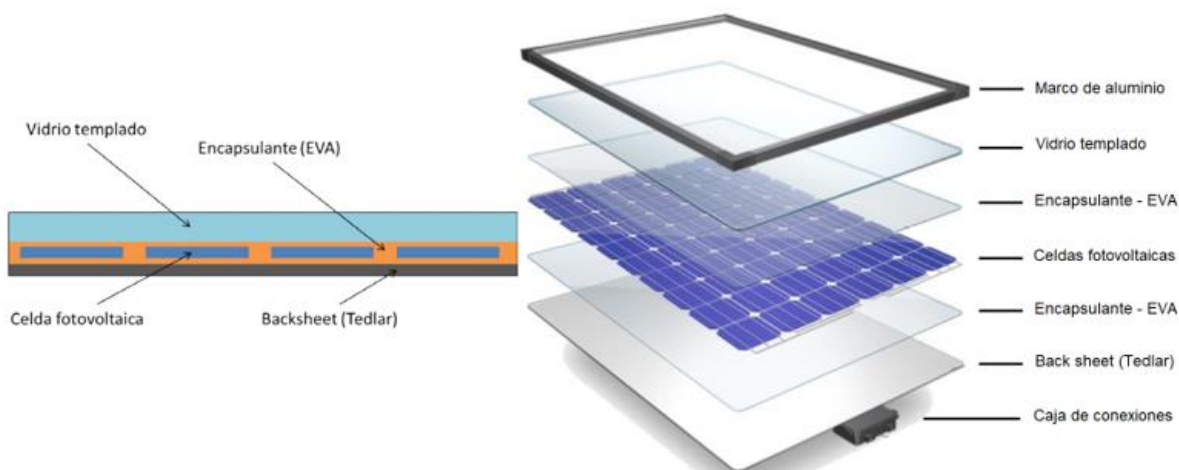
Componentes de un panel fotovoltaico típico; vista transversal (izquierda) [5] y vista 3D (derecha) [2].
